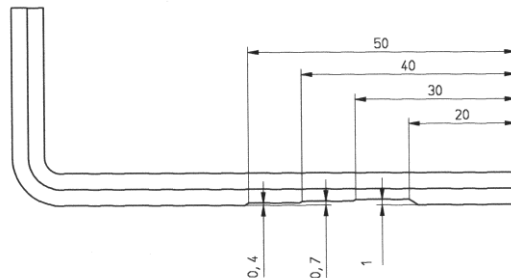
Innensechskantschlüssel mit Einkerbungen
